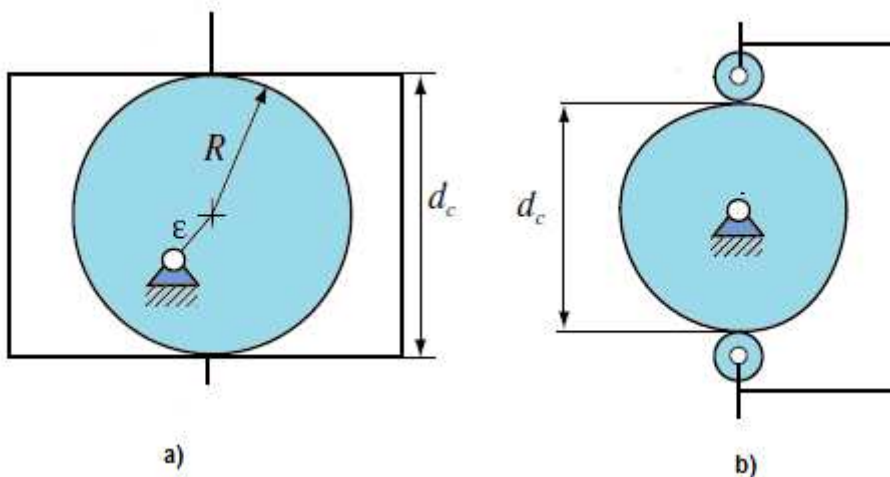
Mecanismos de levas: a) de anchura constante, b) de diámetro constante
